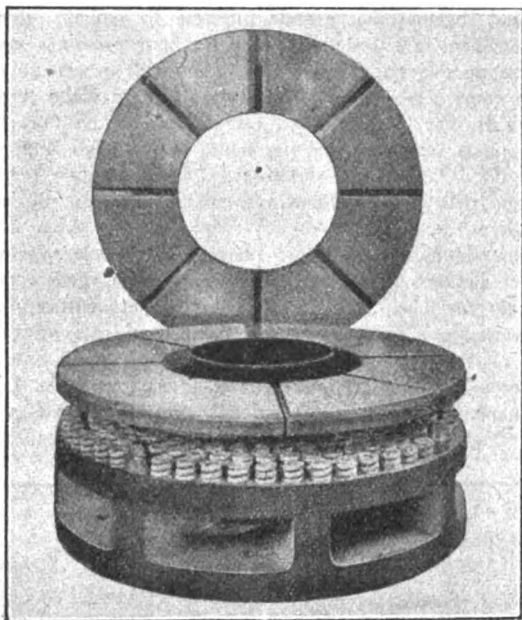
Parti componenti il supporto superiore di un turbo generatore idraulico.
